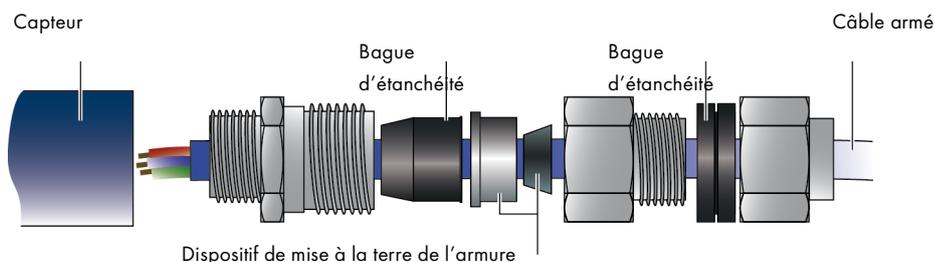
exemple de presse étoupe double compression pour serrage sur câble armé
